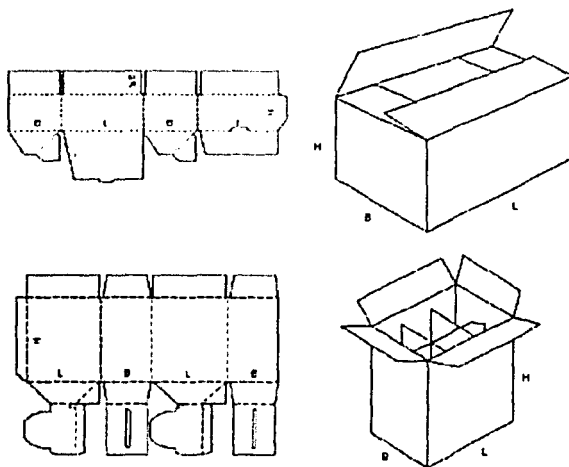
Cajas de fondo automático(www.wellpappe.at)
